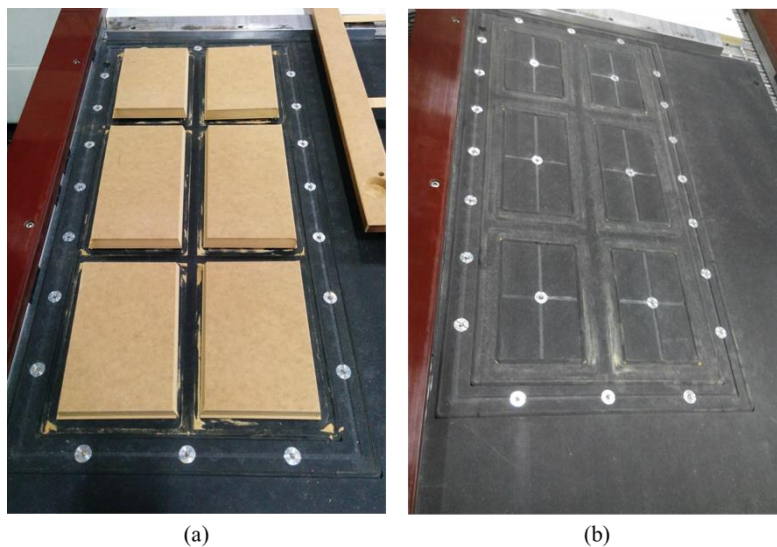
a) Molde após fresagem. b) Molde após aspiração
